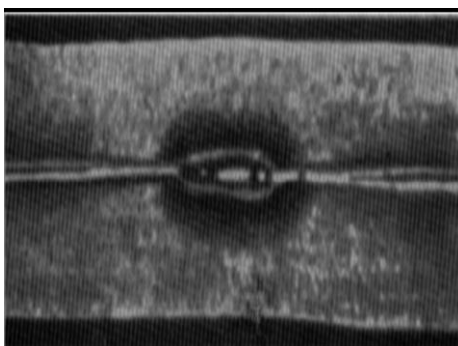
Макроструктура непроваренной сварной точки
